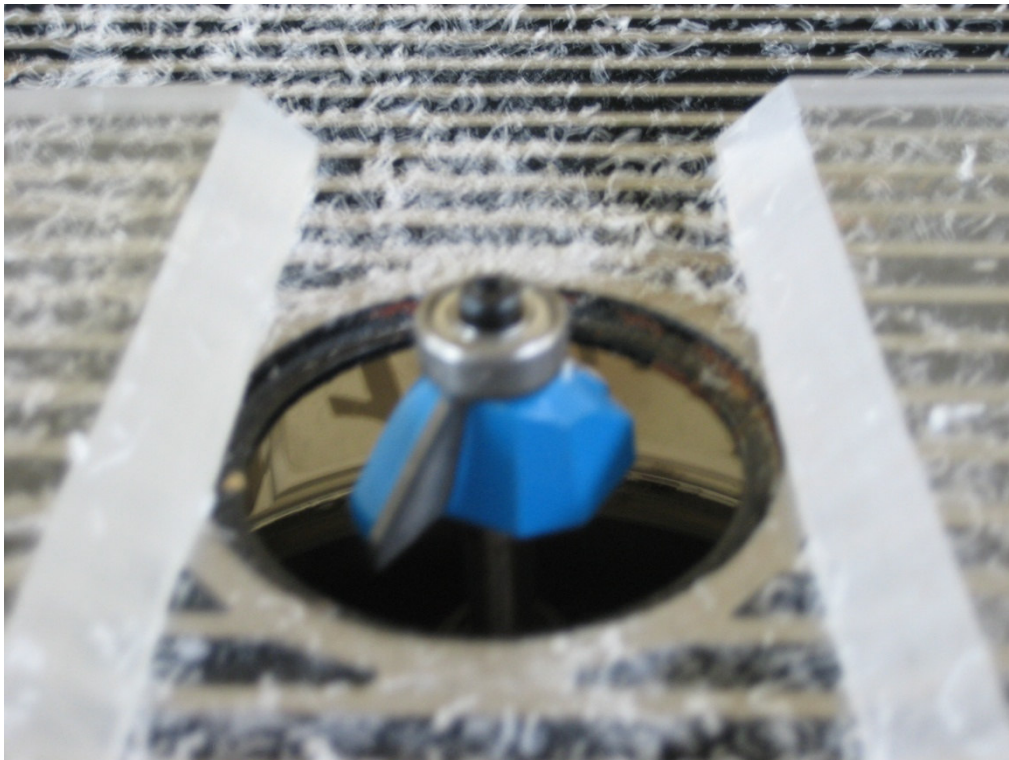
Construcción de vertederos. Detalle del bisel en la cresta del vertedero.
